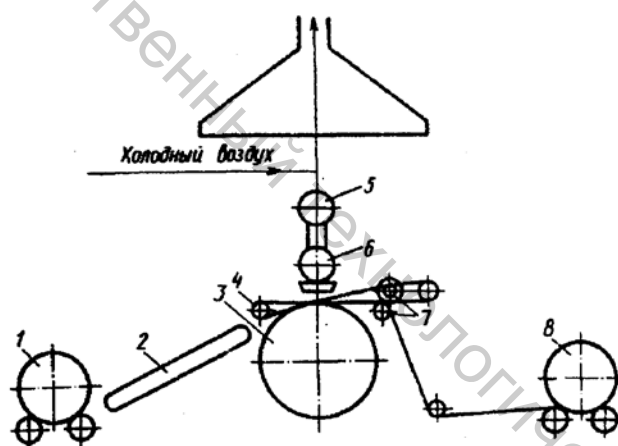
Схема установки УТС-1800 для получения нетканых материалов тепловой контактной сваркой
